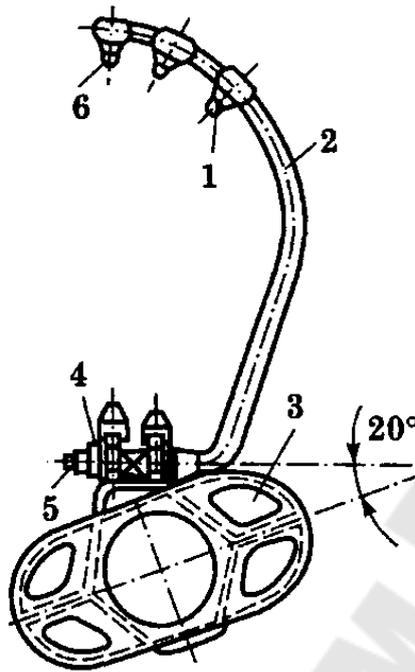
Монтёрские когти: 1 - шип малый; 2 - серповидная скоба; 3 - подножка; 4 - гайка, крепящая хвостовик скобы в проушинах стремени; 5 - стопорное кольцо; 6 - шип большой
